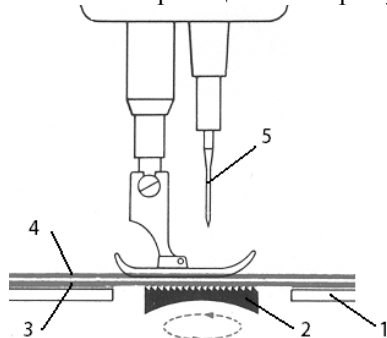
Схема одинарного рейкового механізму: 1 – голкова пластина; 2 – зубчатий пересувач; 3 – нижній шар тканини; 4 – верхній шар тканини; 5 – голка
